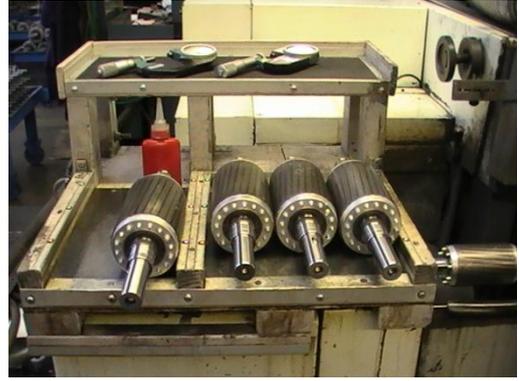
Disposizione degli attrezzi sull'isola Emmerre (b)
